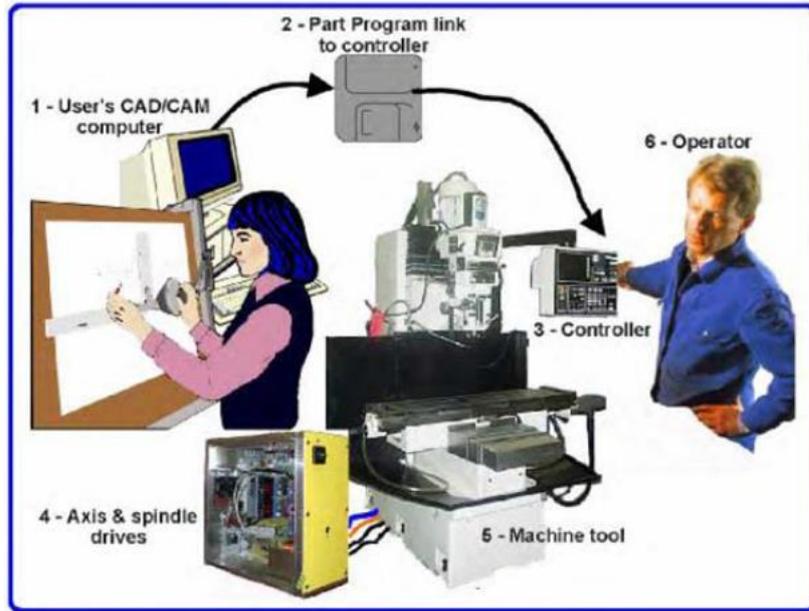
Típico sistema de manufactura CAD / CAM / CNC
